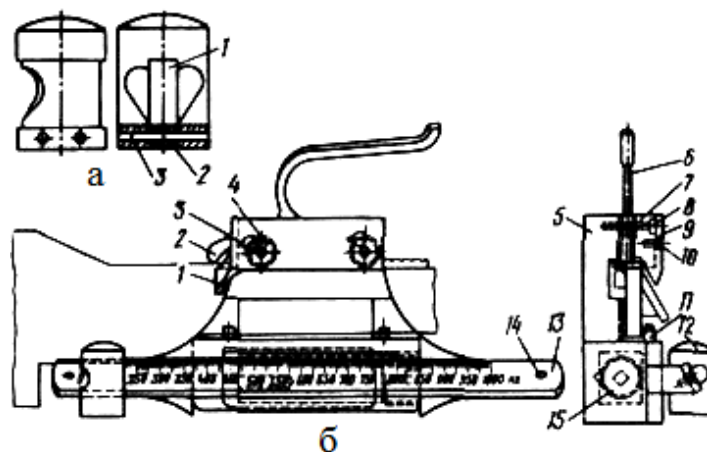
Пересувна гиря: а – сталева: 1 – паз; 2 – сухар; 3 – заклепка; б – стаціонарних ваг: 1 – покажчик; 2 – зуб; 3 – закріплювач; 4 – ролик; 5 – корпус; 6 – рукоятка; 7 – пластина; 8, 10, 14 – гвинти; 9 – кришка; 11 – пробка; 12 – додаткова гиря; 13 – лінійка; 15 – порожнина
